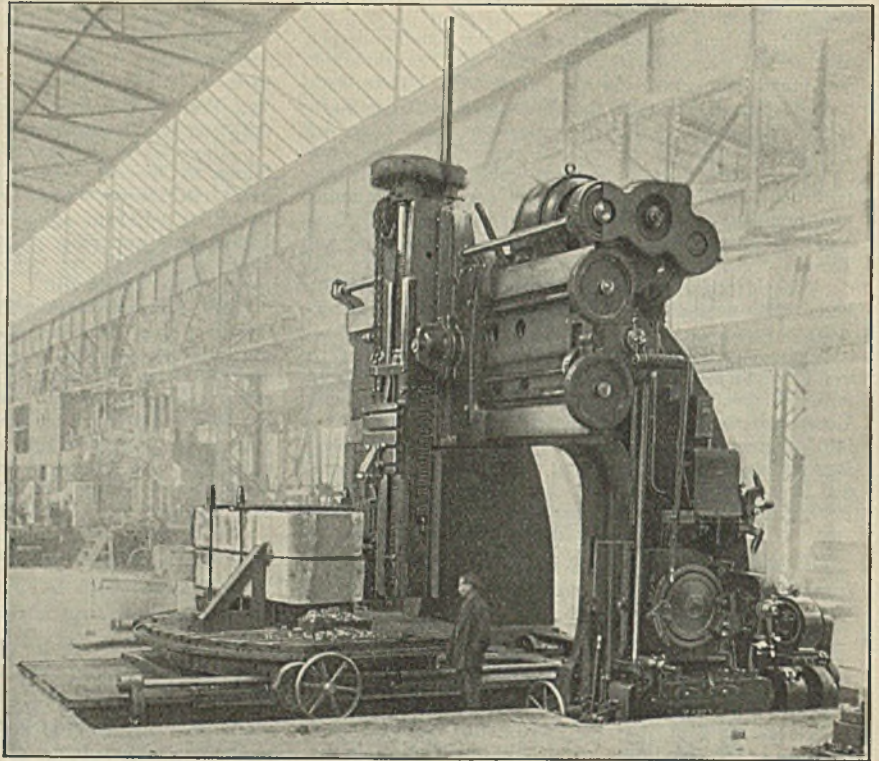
Schweres Portalstoßwerk, gebaut von der Werkzeugmaschinenfabrik Ernst Schieß A. G., Düsseldorf.
